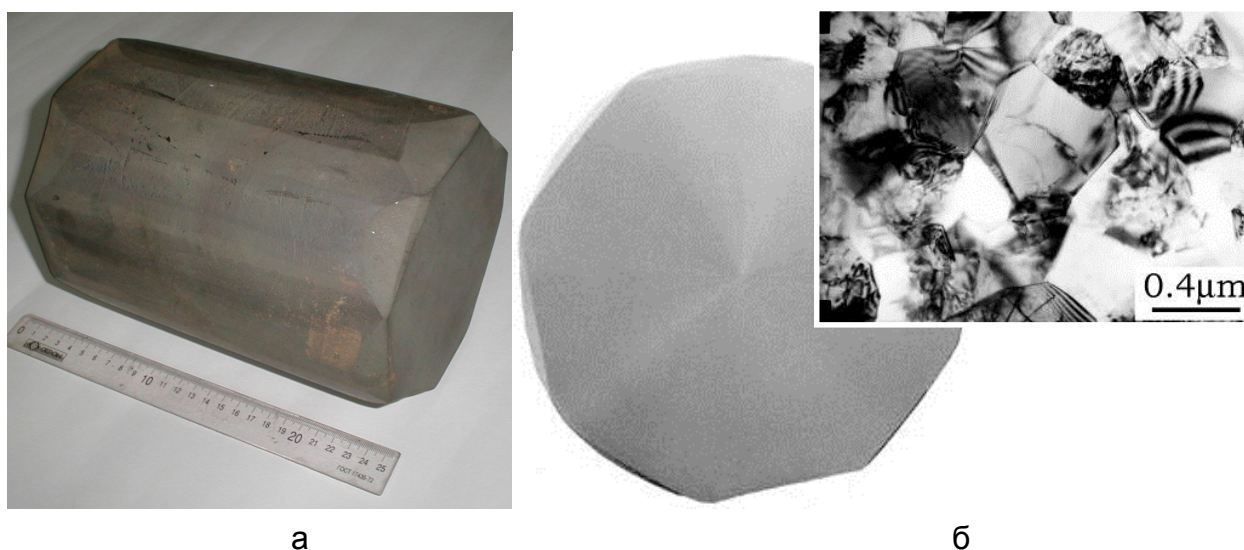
Заготовка, полученная ВИД в интервале 700-550°C. Внешний вид (а); макро- и микроструктура (б).
